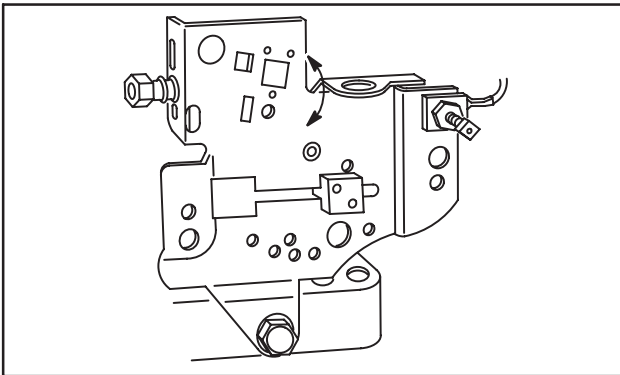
170400, 171400, 190400, 194400, 195400, 221400, 222400, 252400, 254400 avec commande à crémaillère après date de Code 83121500, sauf 253400, 255400
